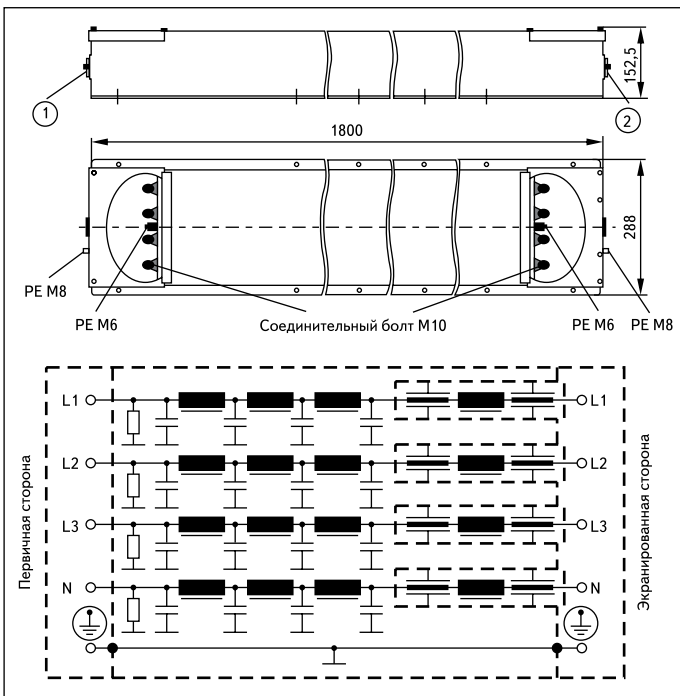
Габаритные размеры и схема силового трехфазного фильтра фирмы EPCOS
